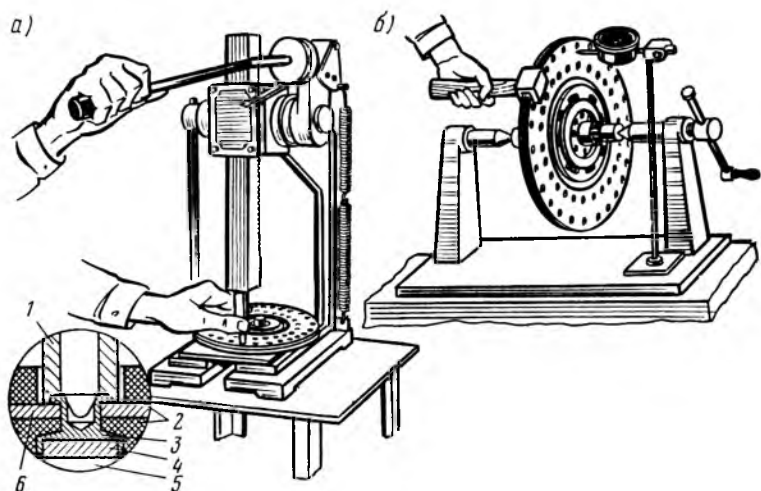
Приспособления для ремонта ведомого диска сцепления:
